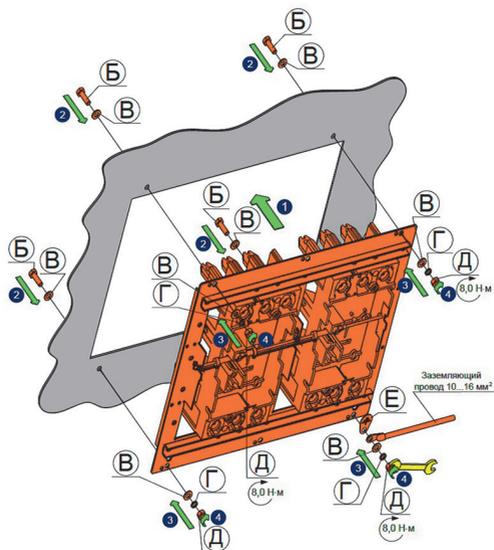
Подготовка рамы механической блокировки для установки выключателей втычного исполнения
